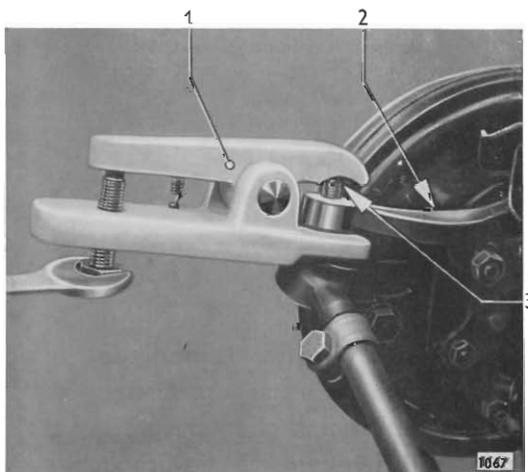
Kugelbolzen aus Lenkhebel herausdrücken
